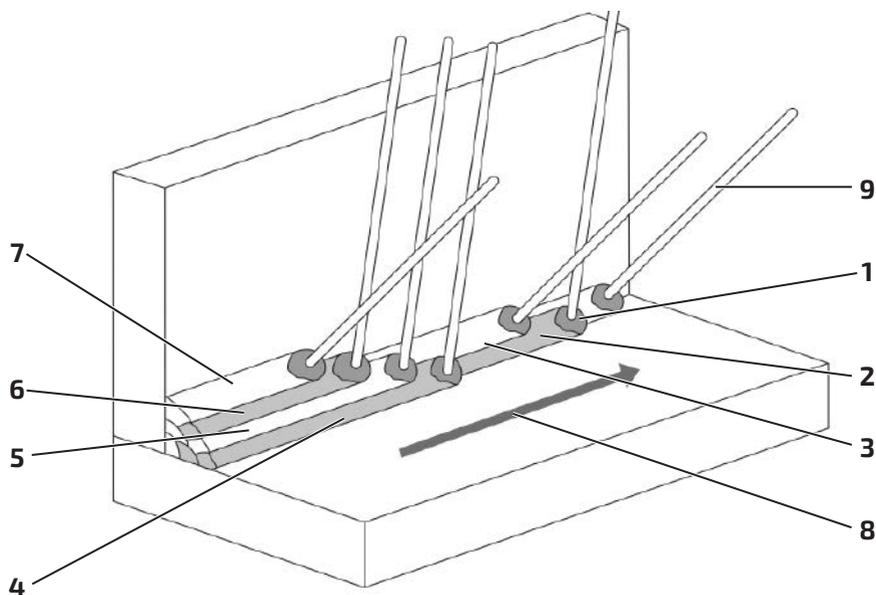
Пример выполнения сварочных швов.
